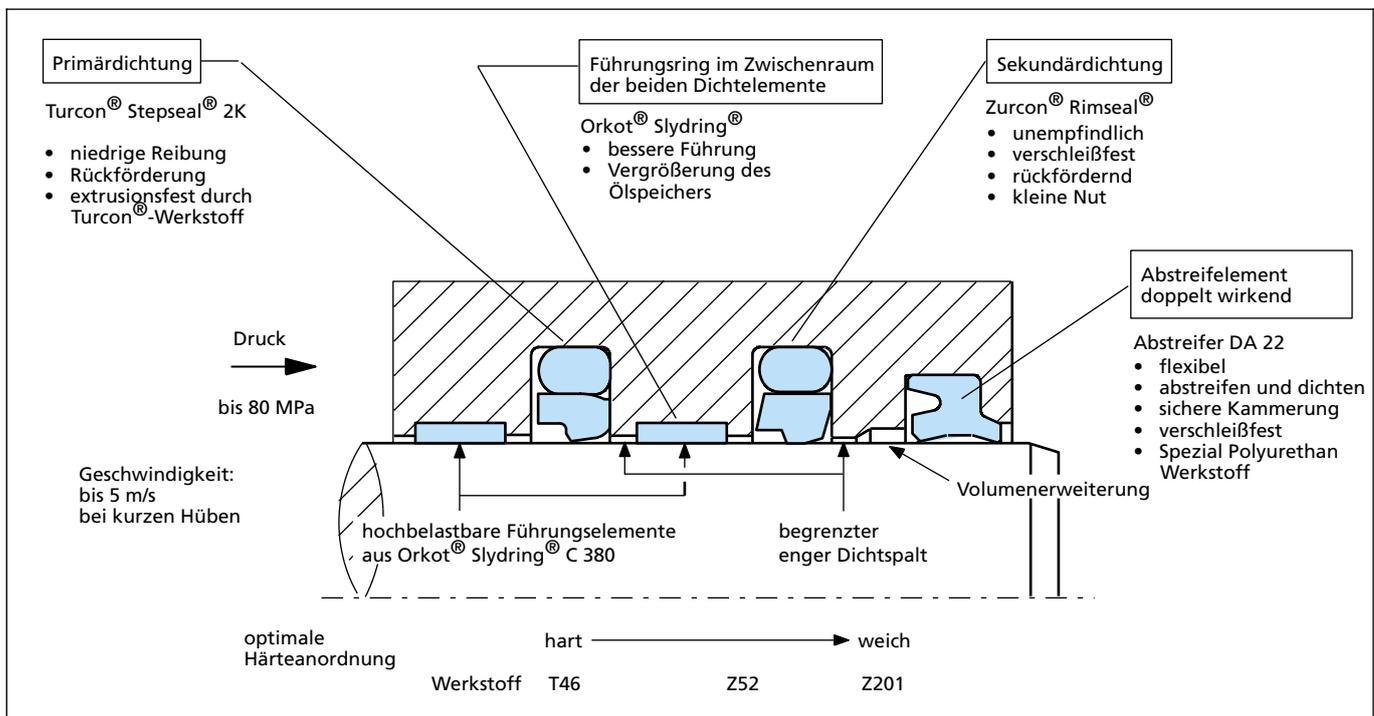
Beispiel für ein redundantes Baukasten-Dichtsystem
